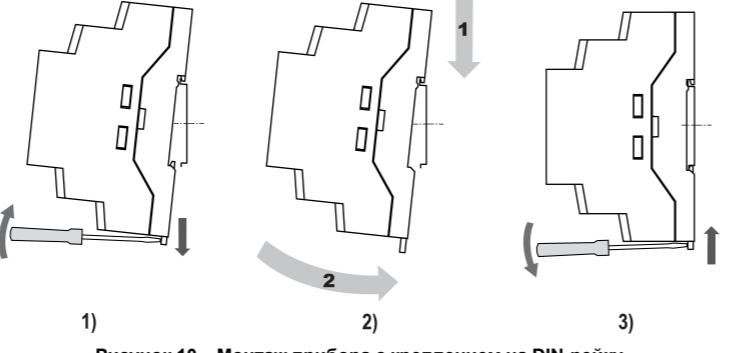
Монтаж прибора с креплением на DIN-рейку
